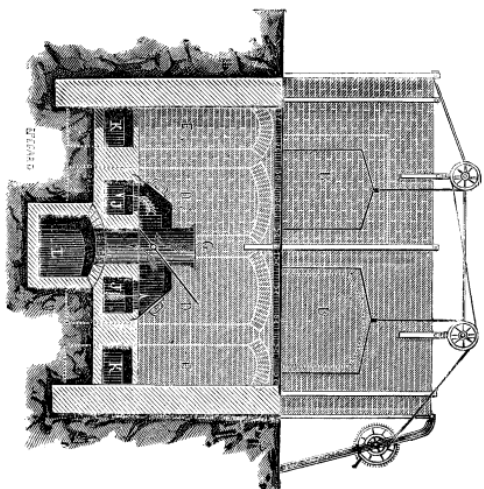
Elevation du four et coupe dans la chambre à valves St. Alb.
